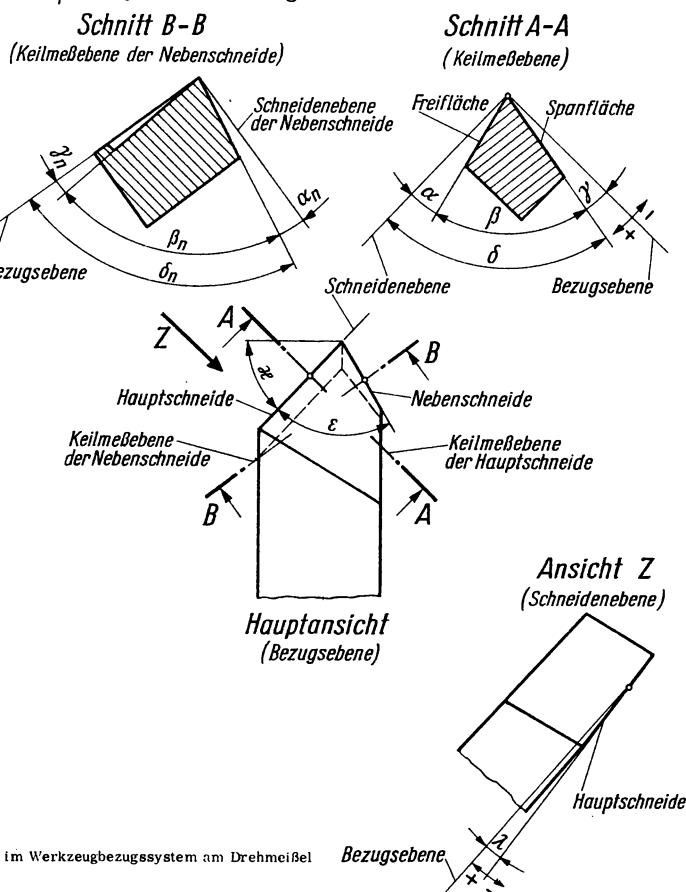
Winkel im Werkzeugbezugssystem am Drehmeißel
